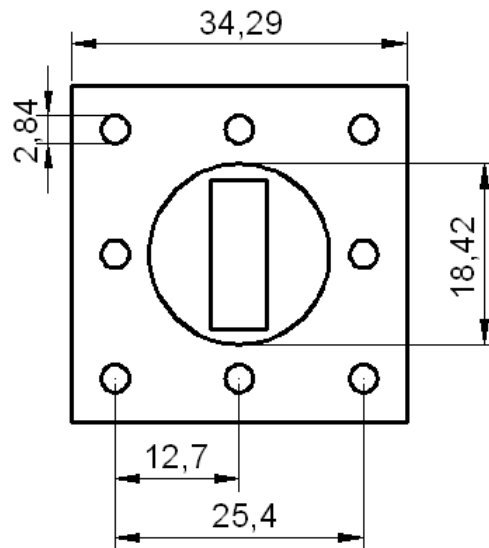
Dimensiones de la placa base para el dissipador de 165kip (cm).
